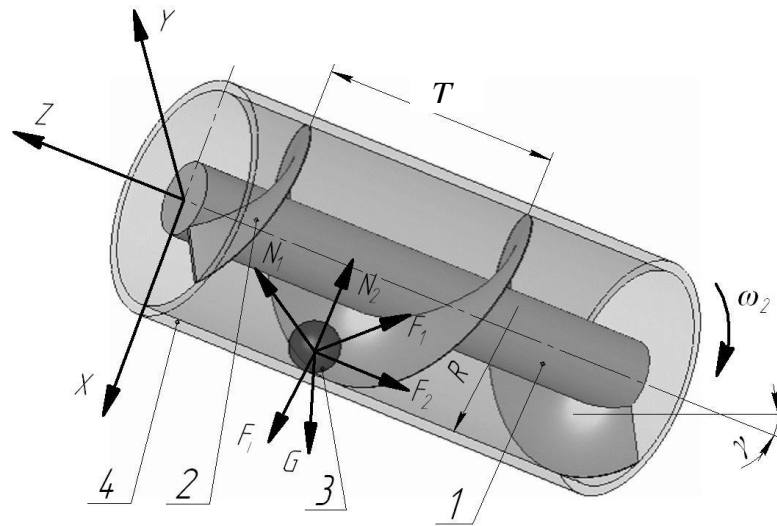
Розрахункова схема для визначення мінімальної частоти обертання циліндричного кожуха гвинтового конвеєра: 1 - вал; 2 – гвинтовий робочий орган; 3 – частинка матеріалу; 4 – обертовий циліндричний кожух
